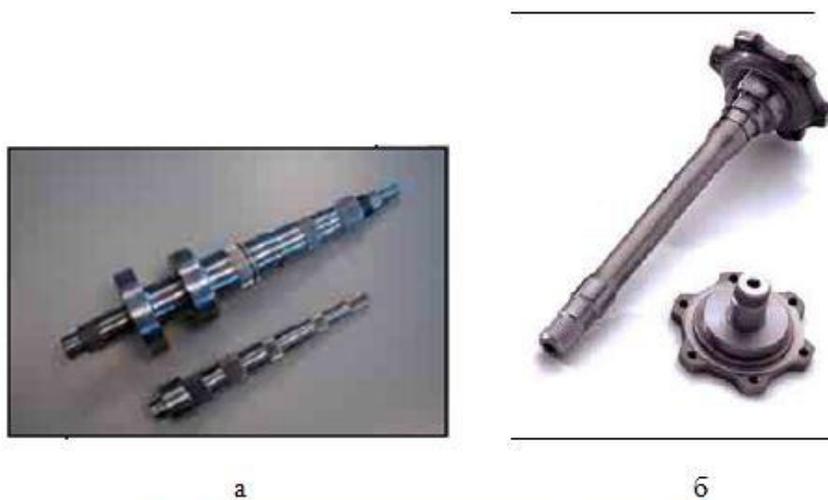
Накатка профилей, фирма Profiroll [5] а – валы коробок передач; б - полуоси
